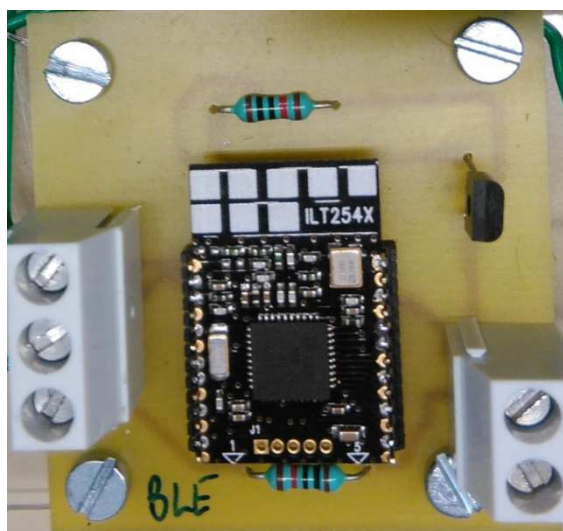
VISTA SUPERIOR DE LA PCB DEL MÓDULO PARA EL SENSADO MEDIANTE BLE
